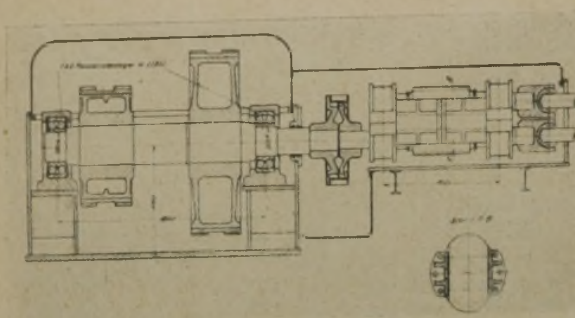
Getriebekasten mit Abtrieb zum Duo-Kammwalzgerüst einer Drahtstraße
